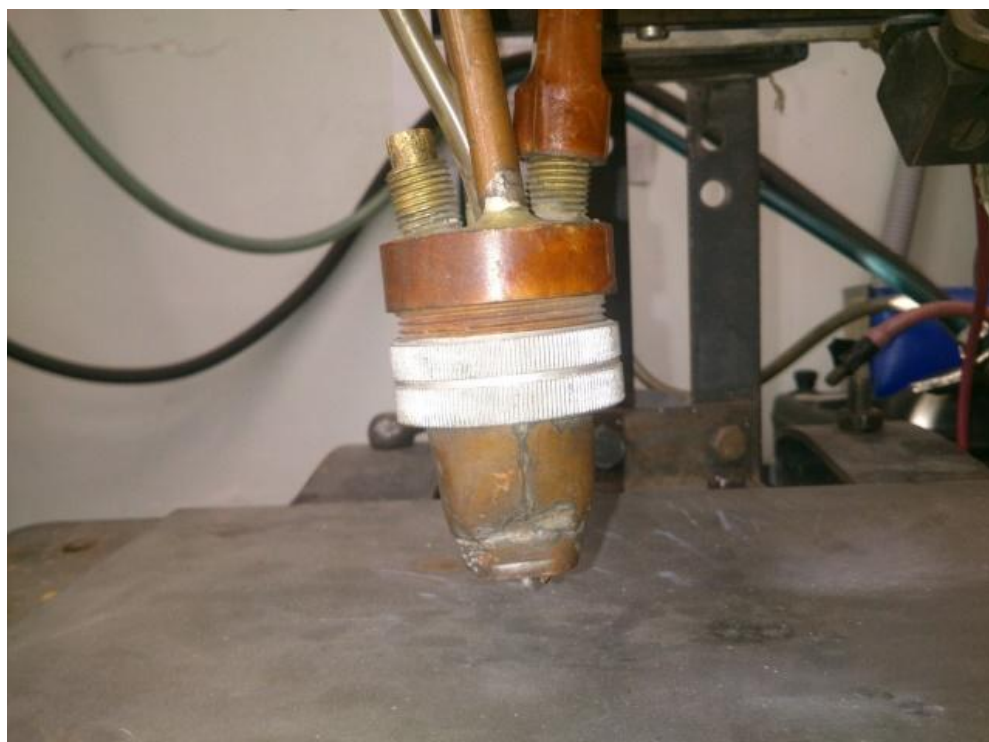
Внешний вид горелки для сварки неплавящимися электродами ГС-5А
